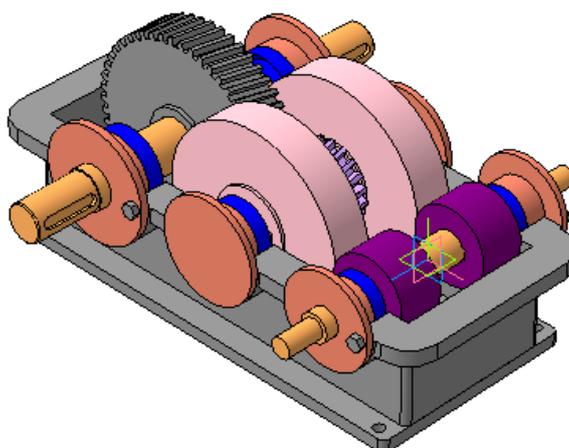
Внешний вид косозубого редуктора станка-качалки с раздвоенной быстроходной ступенью.
